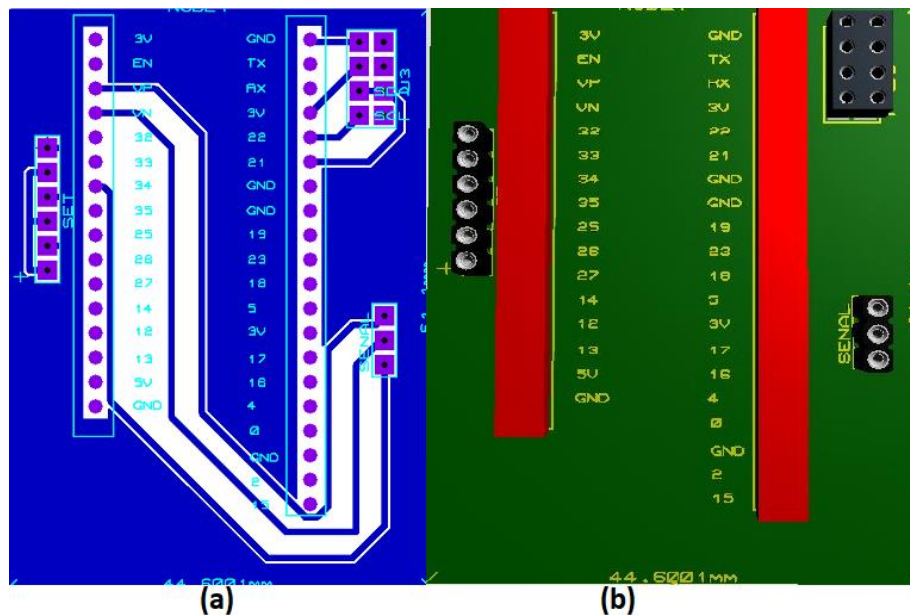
Diseño (a) PCB y (b) diseño 3D, tarjeta adquisición de datos
